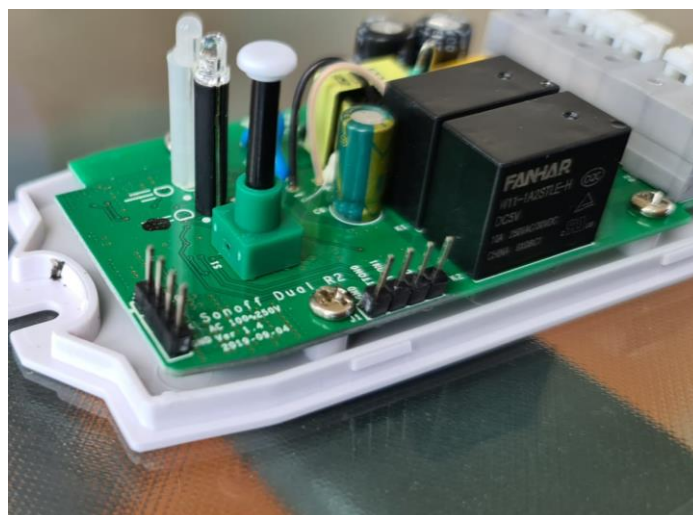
Pines soldados placa SOnOff Dual R2
